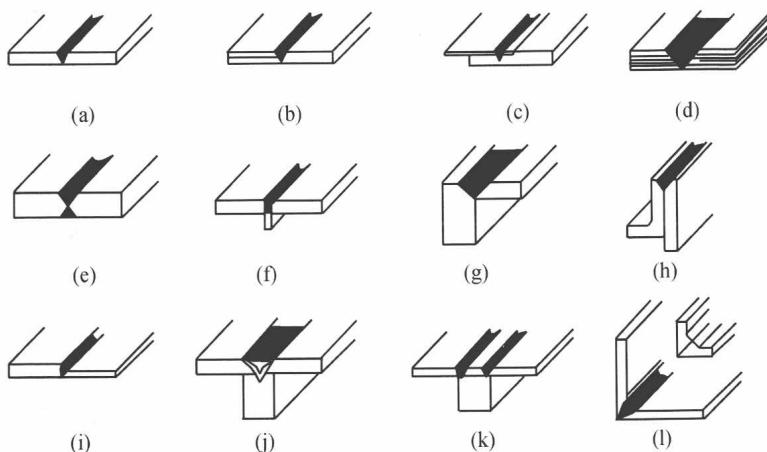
搅拌摩擦焊接常用的接头形式
